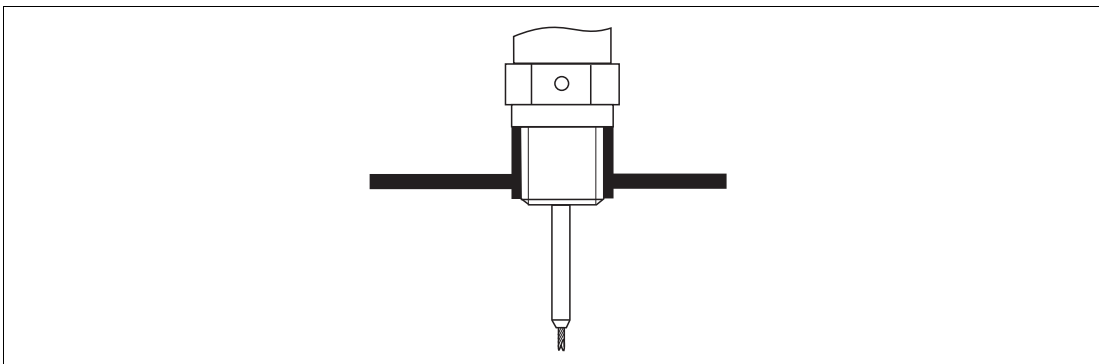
Montage mit Einschraubgewinde; bündig mit der Behälterdecke
